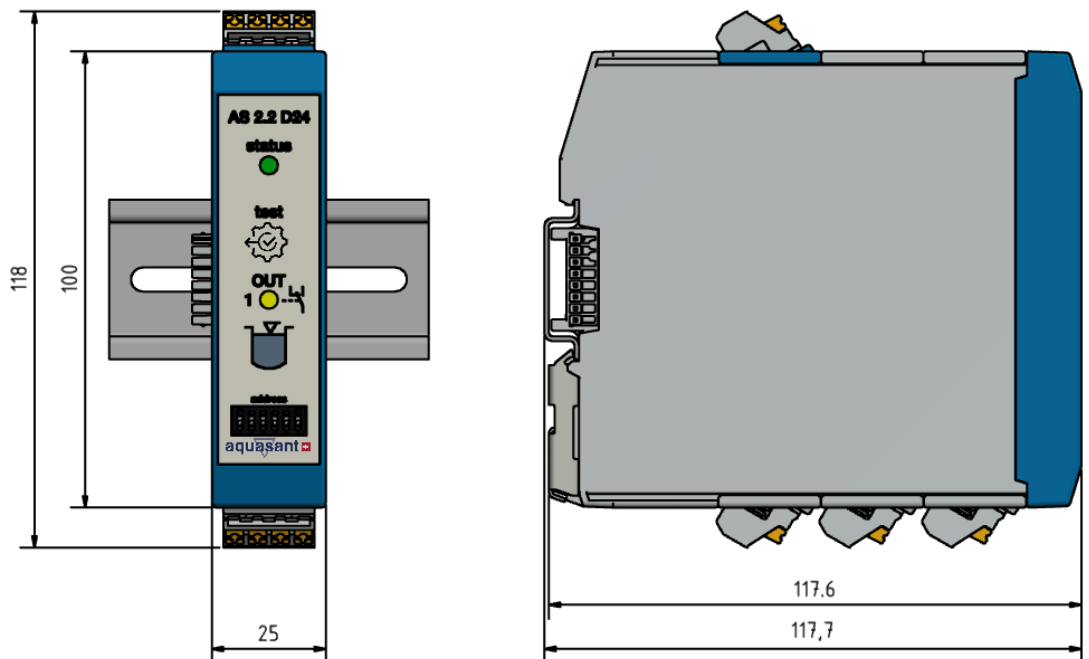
Gerätedimensionen, Auf-, Seitenansicht
